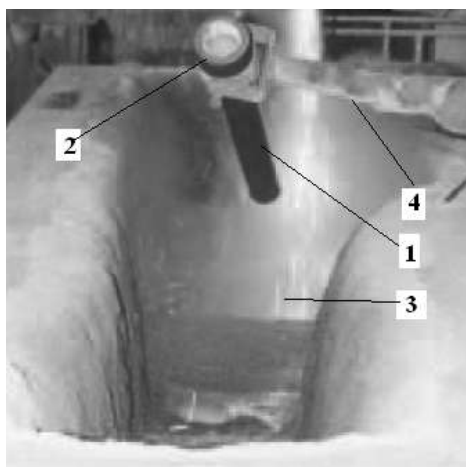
Установка манипулятором защитной трубы сталеразливочного ковша в промежуточном ковше:
